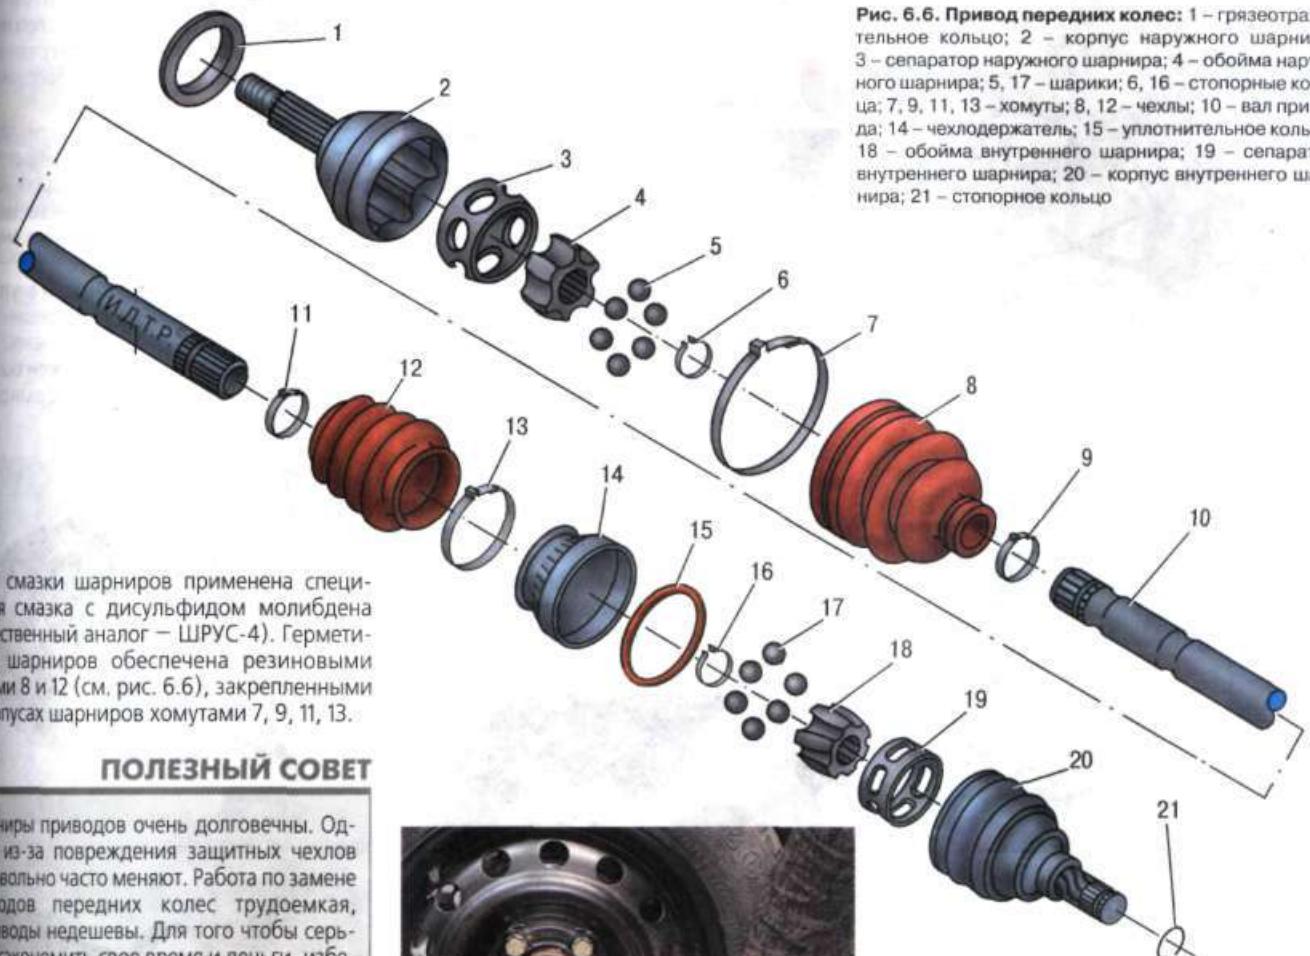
Привод передних колес: 1 – грязеотражательное кольцо; 2 – корпус наружного шарнира; 3 – сепаратор наружного шарнира; 4 – обойма наружного шарнира; 5, 17 – шарики; 6, 16 – стопорные кольца; 7, 9, 11, 13 – хомуты; 8, 12 – чехлы; 10 – вал привода; 14 – чехлодержатель; 15 – уплотнительное кольцо; 18 – обойма внутреннего шарнира; 19 – сепаратор внутреннего шарнира; 20 – корпус внутреннего шарнира; 21 – стопорное кольцо
